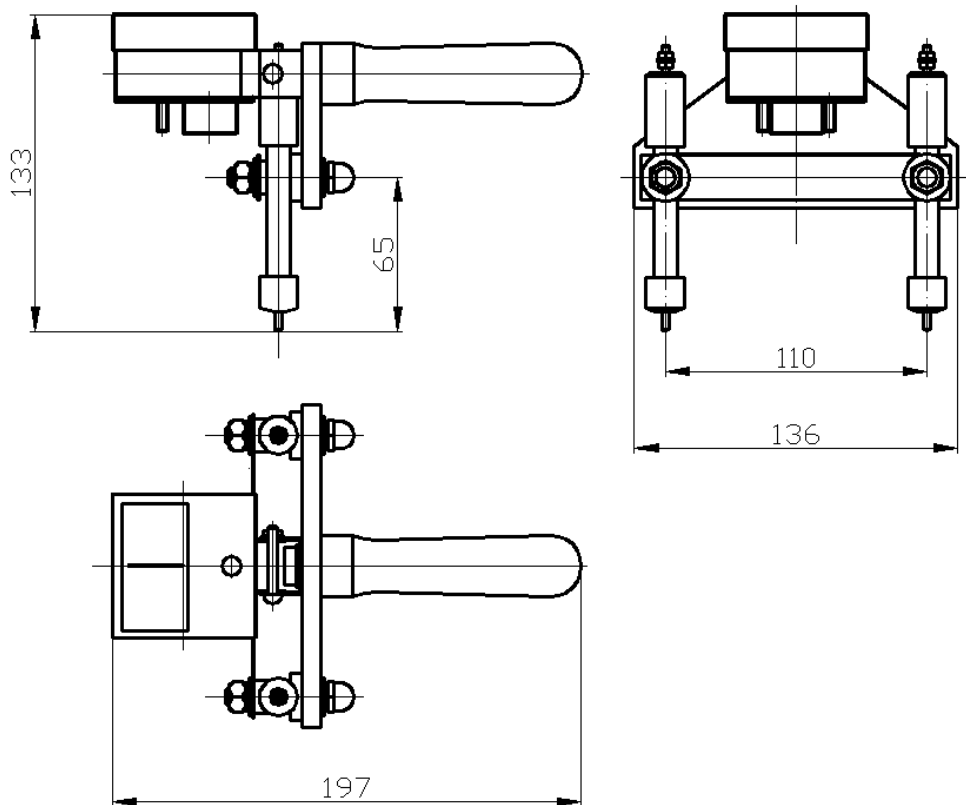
Габаритные размеры вилки нагрузочной ПАЩ-500.
